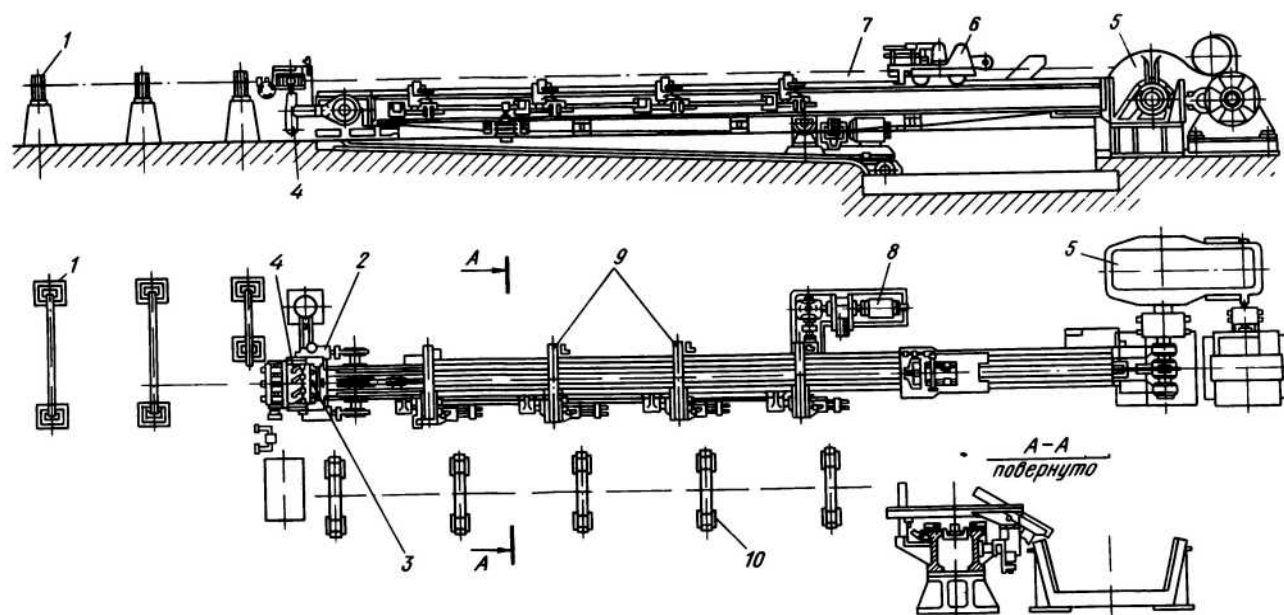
Трехниточный цепной стан для волочения прутков
